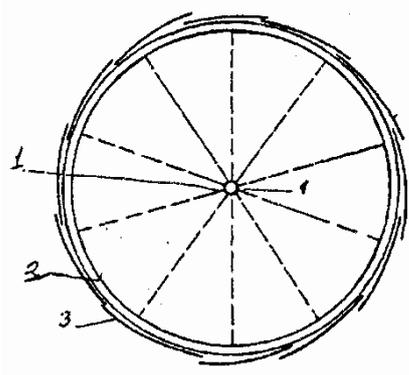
Схема просветки кольцевого стыкового сварного соединения с внешним диаметром 32...64мм через две стенки:
